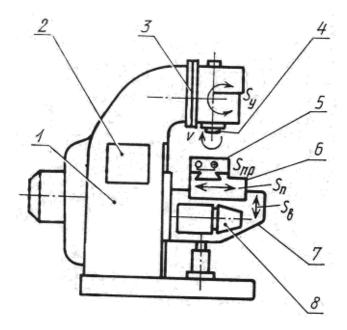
Вертикально-фрезерный станок: 1 — станина; 2 — коробка скорости; 3 — поворотная шпиндельная головка; 4 — шпиндель; 5 — стол; 6 — салазки; 7 — консоль; 8 — коробка подач.
